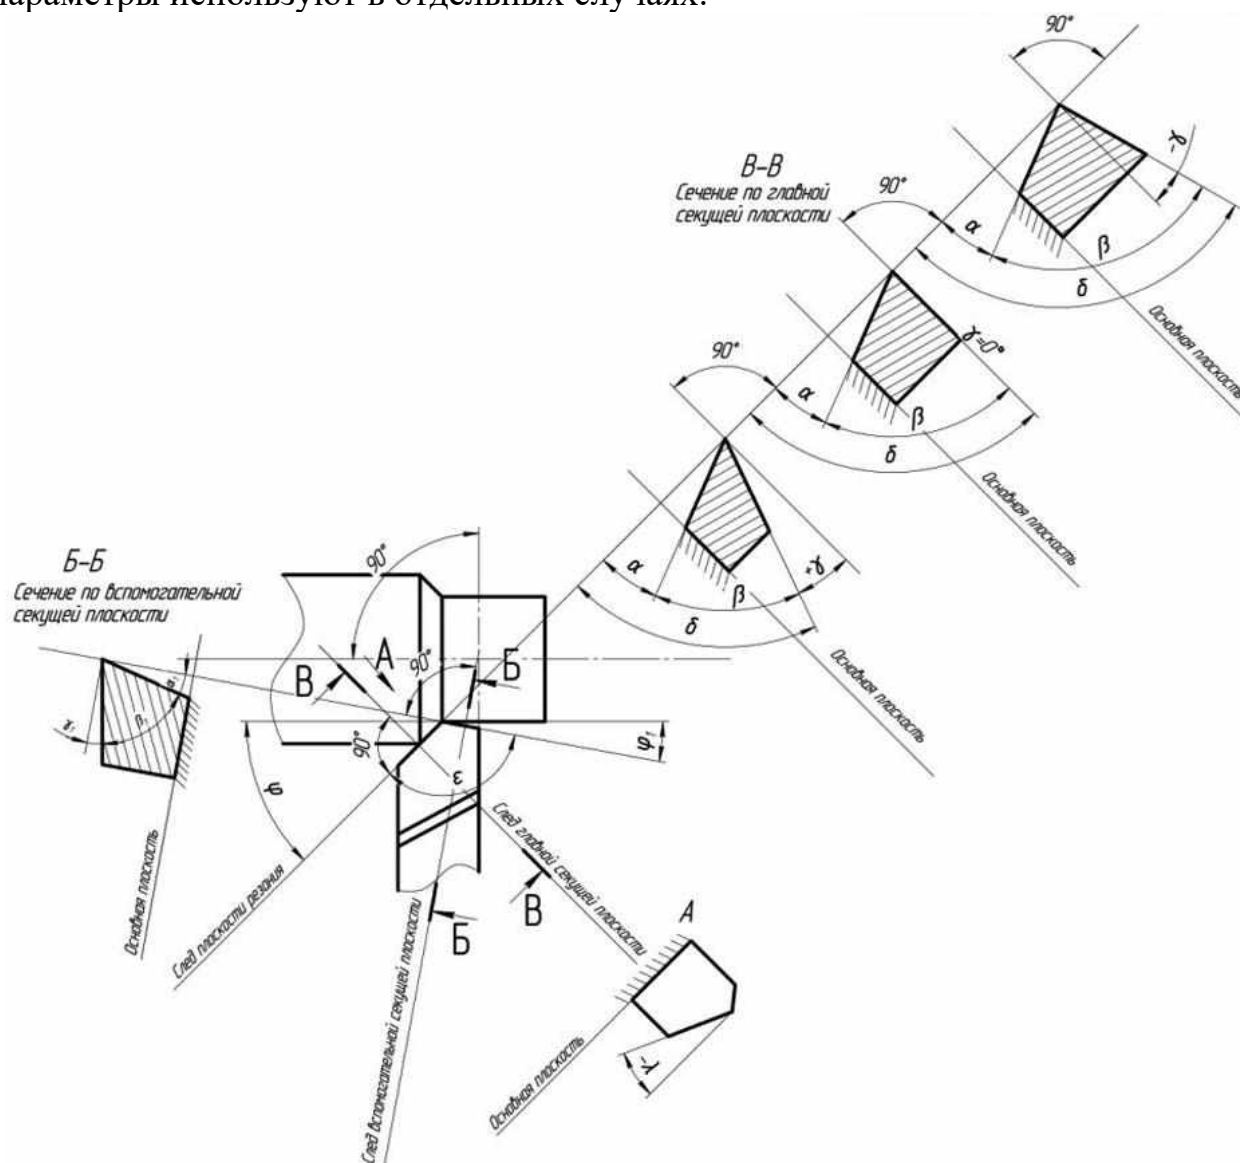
Геометрические параметры режущей части токарного проходного резца [1]
